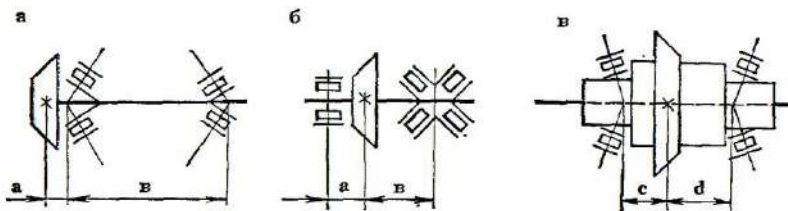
Схеми установки зубчастих коліс і підшипників головної передачі
